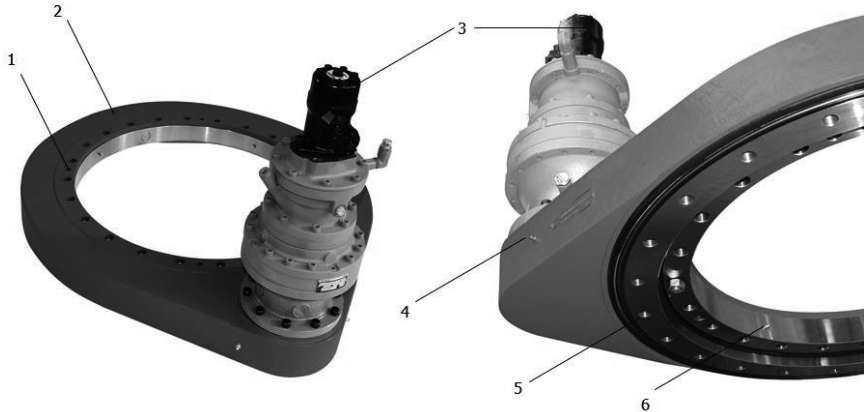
Schwenktrieb SP-H, schwere Ausführung
